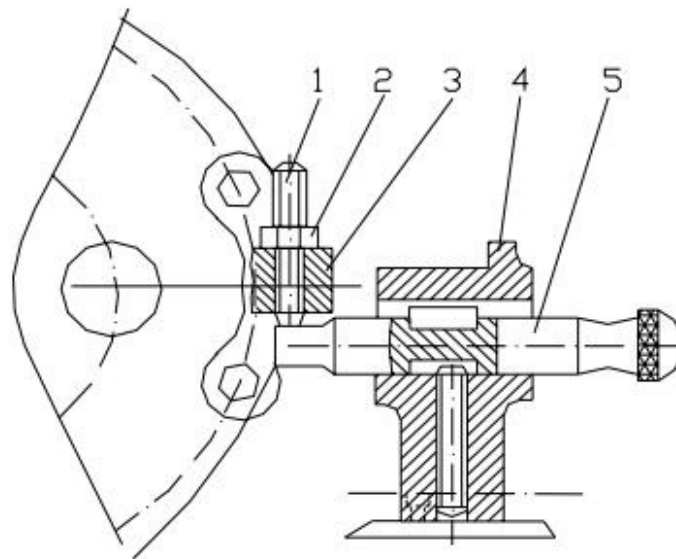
Схема обмежувача кругової подачі револьверної головки
